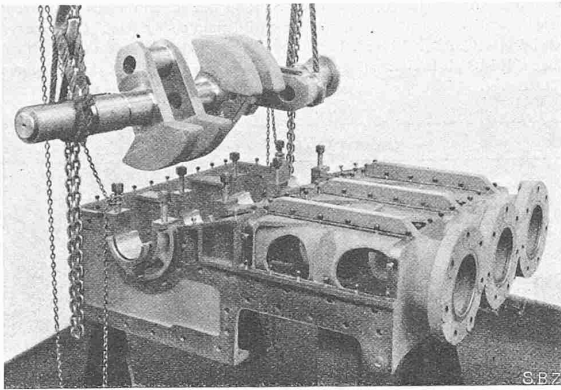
Gestell der Maschine mit abgehobener Kurbelwelle.
